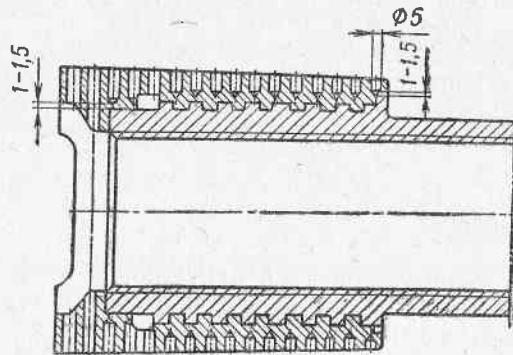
Подготовка дульного тормоза к разрезке (сверление отверстий для продольного разреза)
